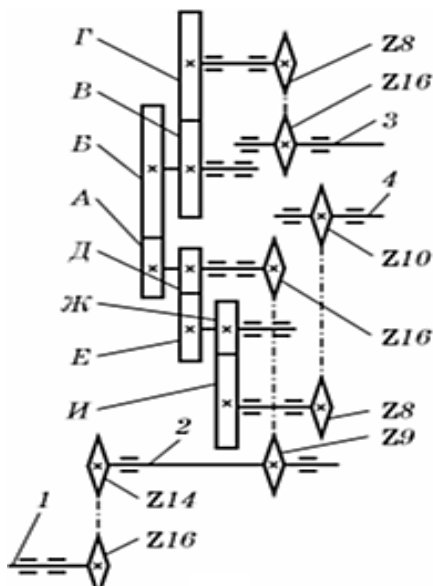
Механізм передачі сівалки СЗ-3,6А:
